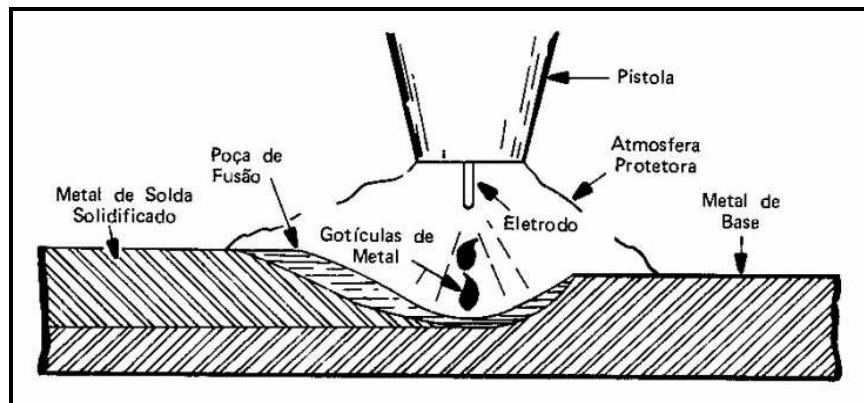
Esquema do processo de soldagem FCAW-G com proteção gasosa. Fonte: Marques et al (2007)
